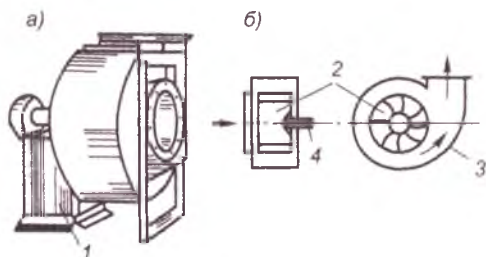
Общий вид (а) и схема устройства (б) центробежного вентилятора
